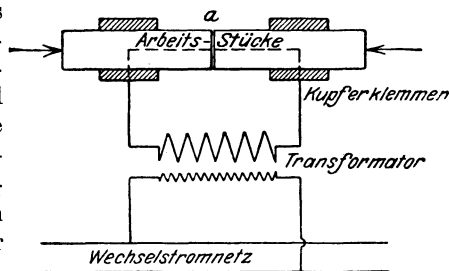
Schema der elektrischen Stumpfschweißung.
